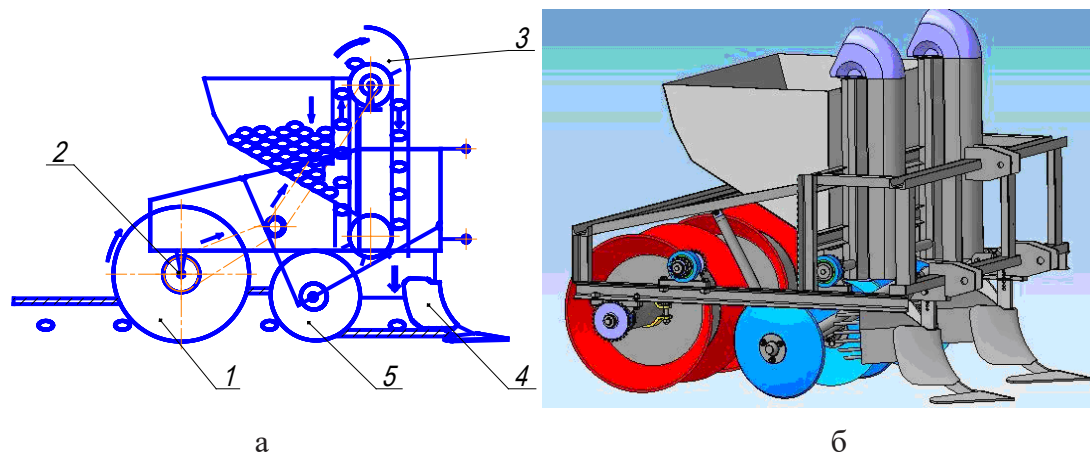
Двухрядная картофелесажалка элеваторной конструкции
